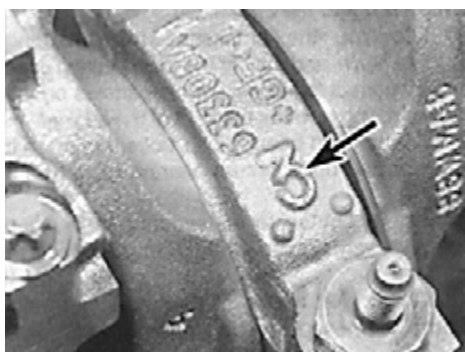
На крышках коренных подшипников большинства двигателей нанесены стрелки, которые указывают на переднюю часть двигателя, и номера крышек, начиная с первого цилиндра.
